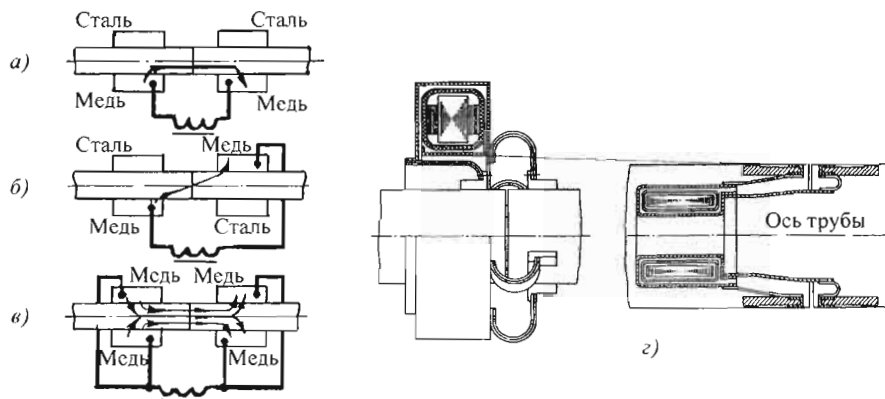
Схемы токоподвода к сварочным губкам стыковых машин:
